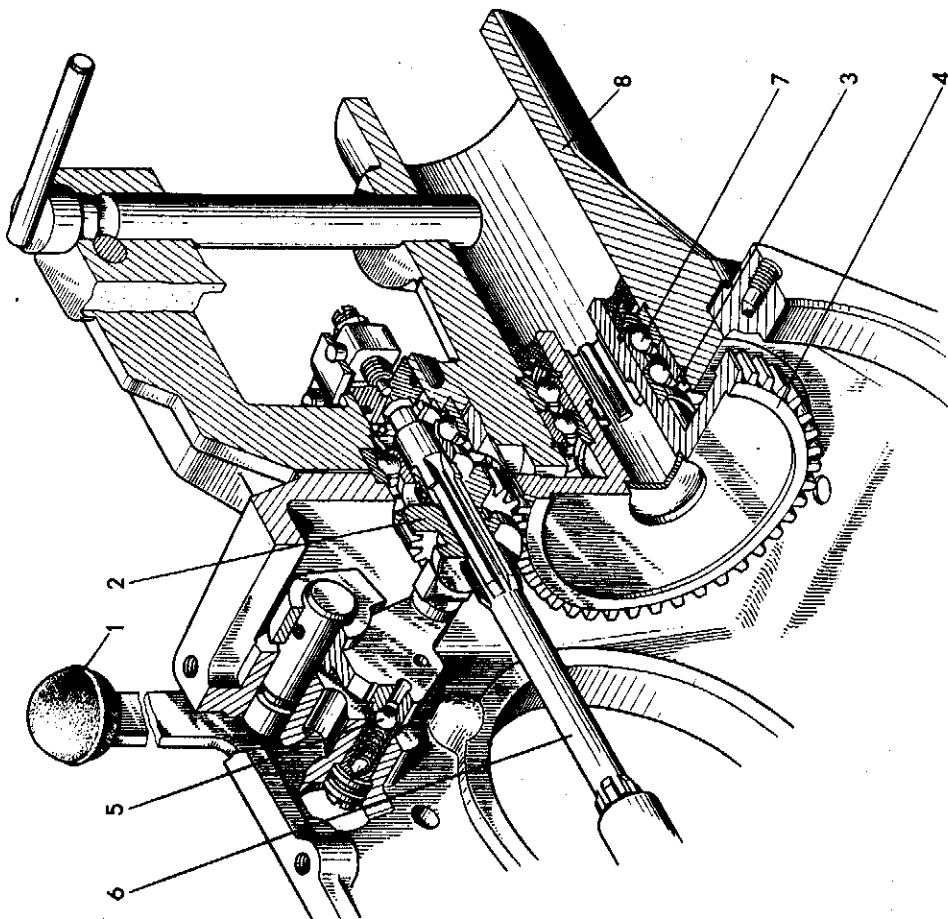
Вал отбора мощности; 1 — рычаг включения ВОМ; 2 — шестерня ведущая; 3 — кольцо стопорное; 4 — шестерня ведомая; 5 — фиксатор рычага включения; 6 — вал; 7 — шарикоподшипник; 8 — корпус.
